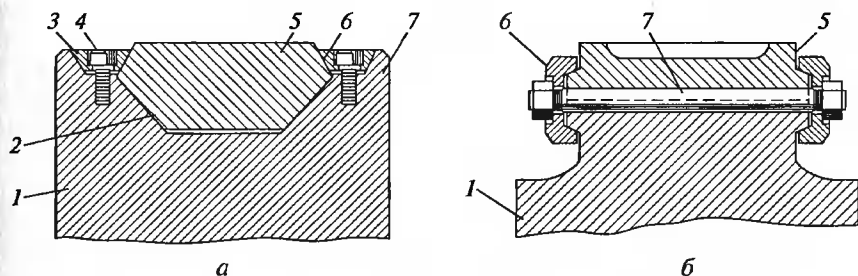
Конструкции прессующего (а) и формующего (б) валков со сменными рабочими элементами:
